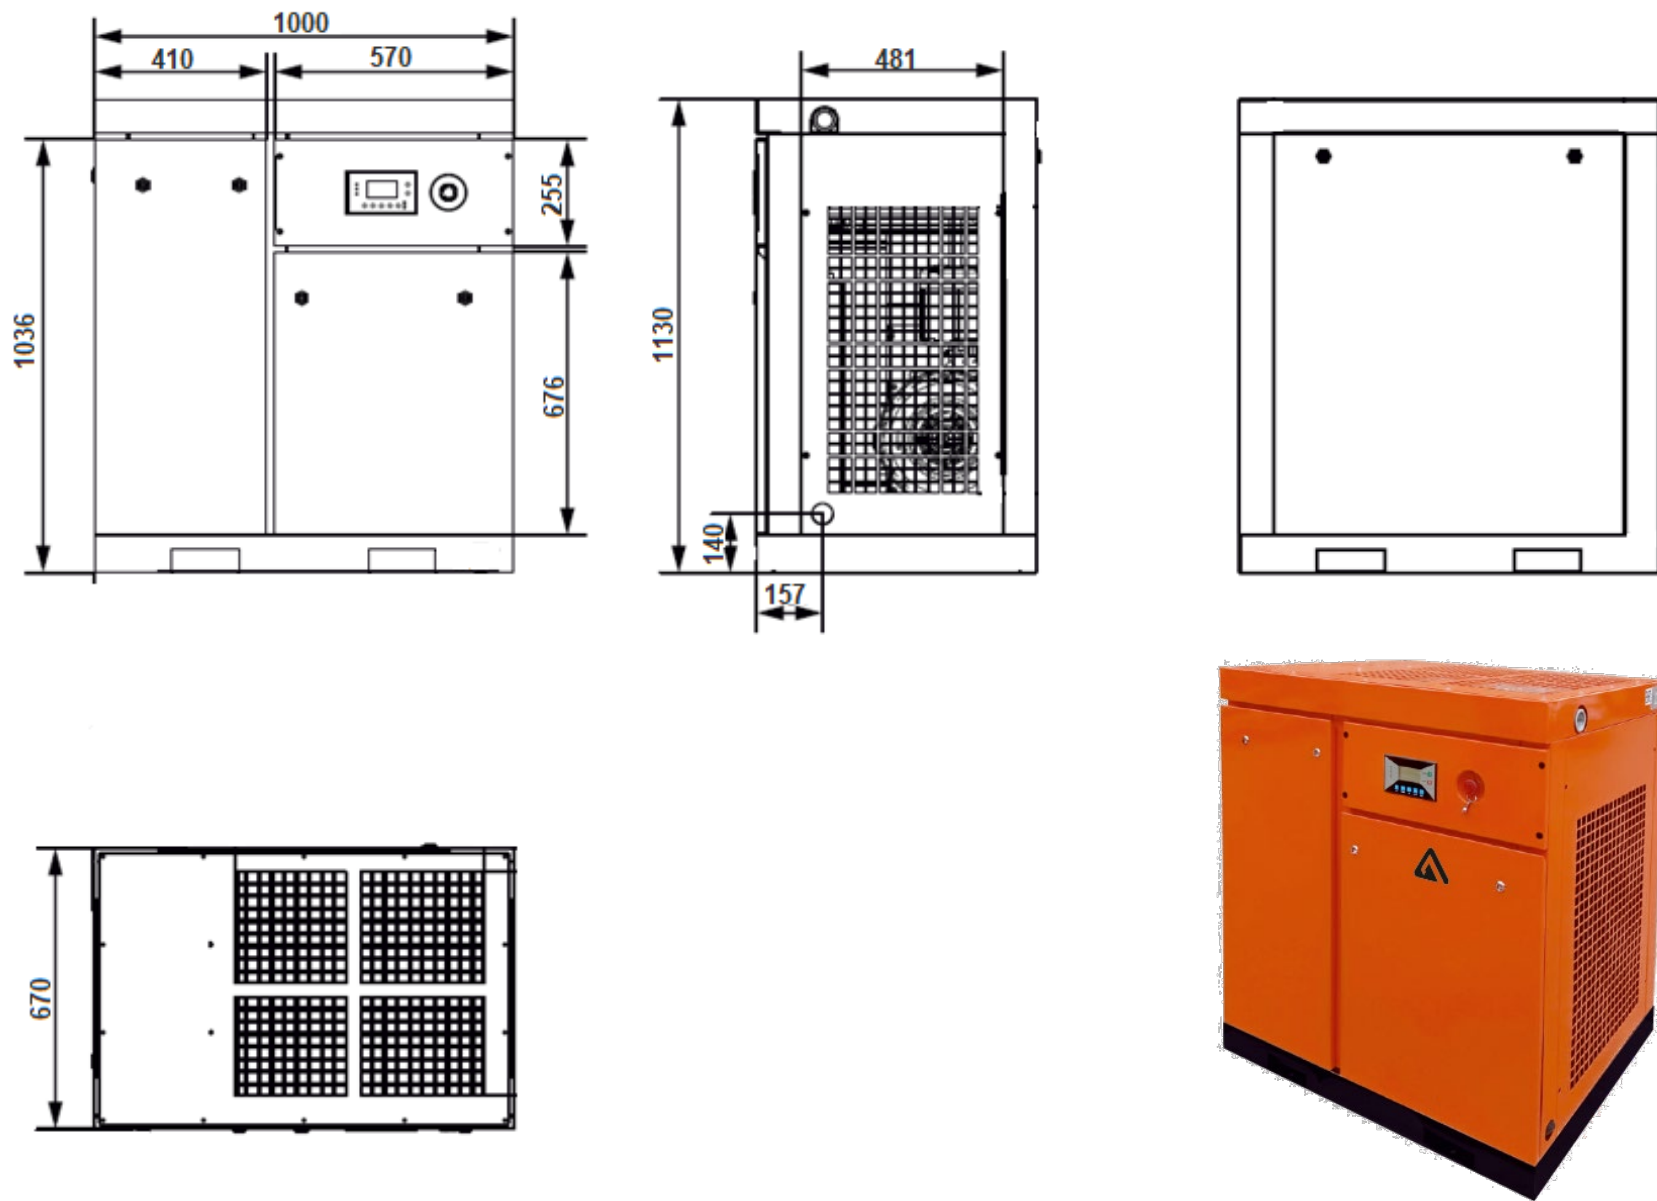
Общий вид, габаритные размеры станции компрессорной ЗИФ-СВЭ типа АРМ с двигателем 22 кВт
